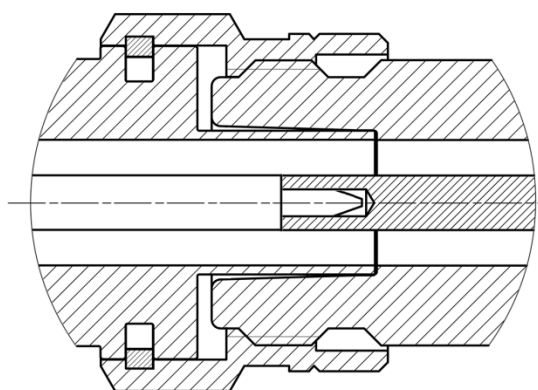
Соединители N и III (розетка справа, вилка слева)
